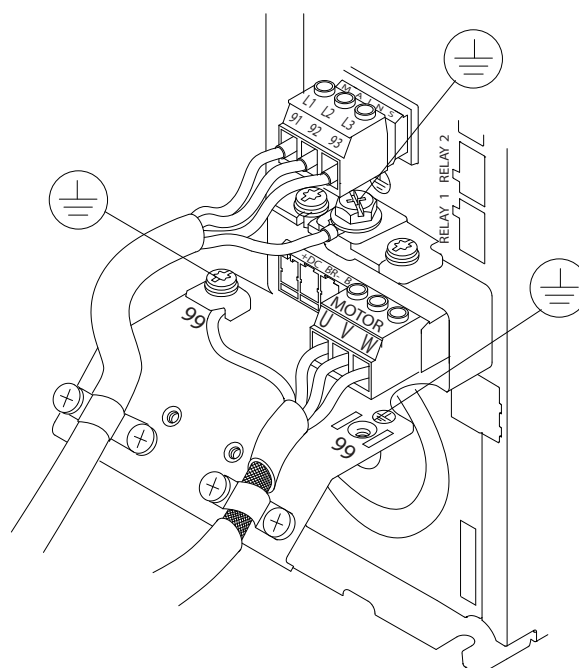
Exempel på kabeldragning för motor, nät och jordning
